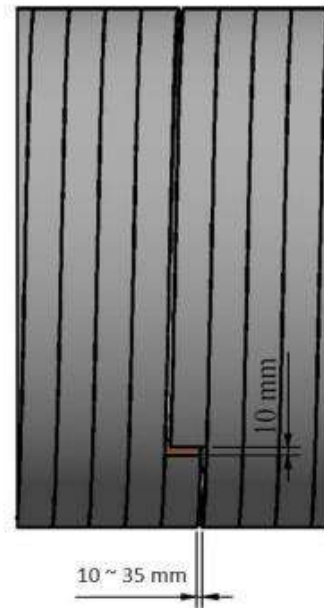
Posicionamento das extremidades dos tubos KANAWEHOLITE antes de serem soldados
